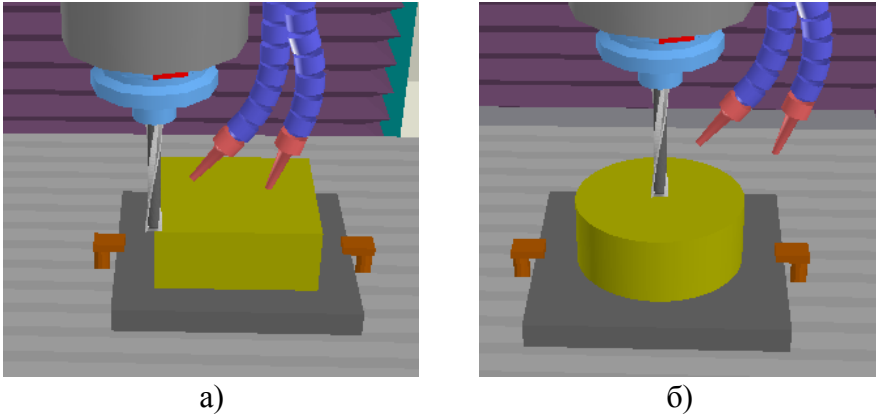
Переміщення в точку прив'язки для заготовки: а) призматичної, б) циліндричної
